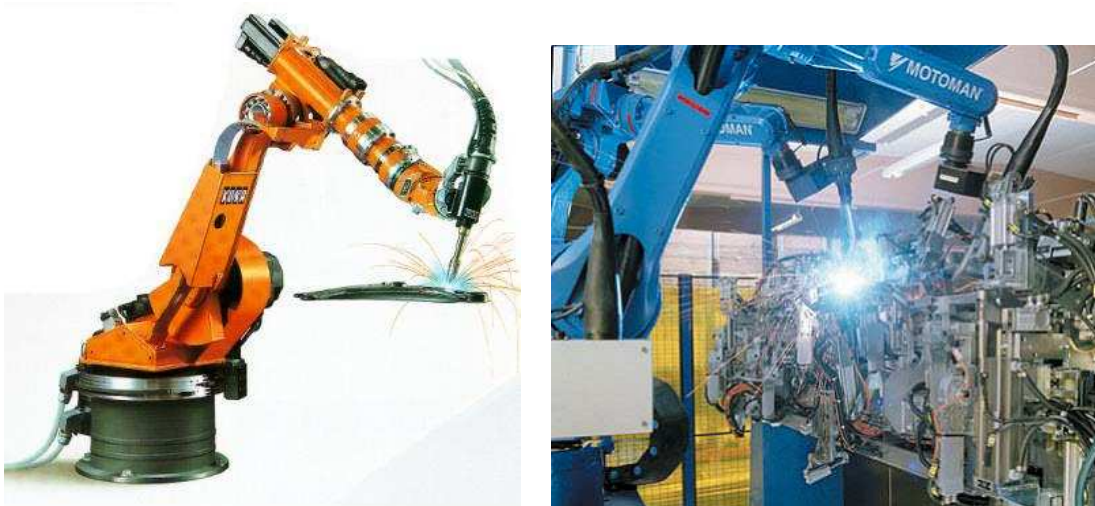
Robot utilizado en la industria para soldadura
